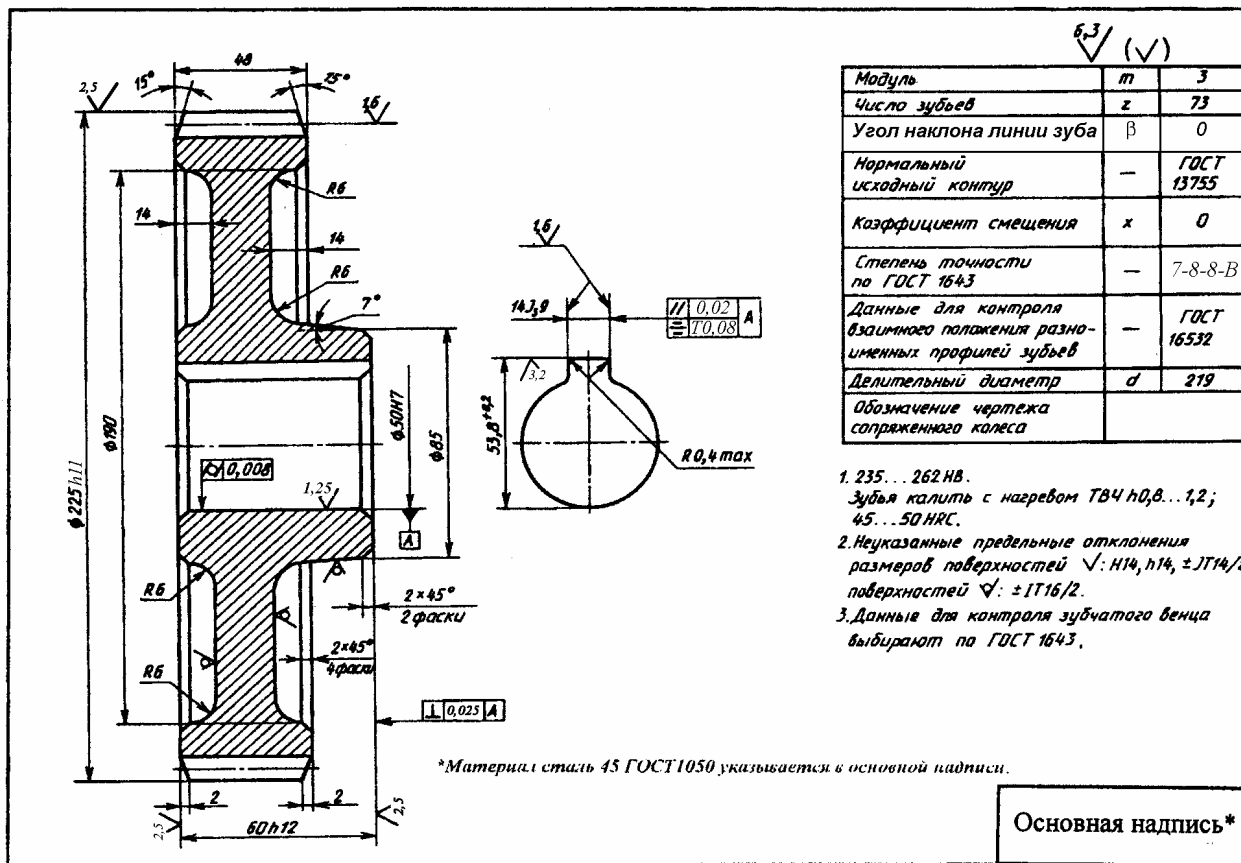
Рабочий чертеж цилиндрического прямозубого колеса
